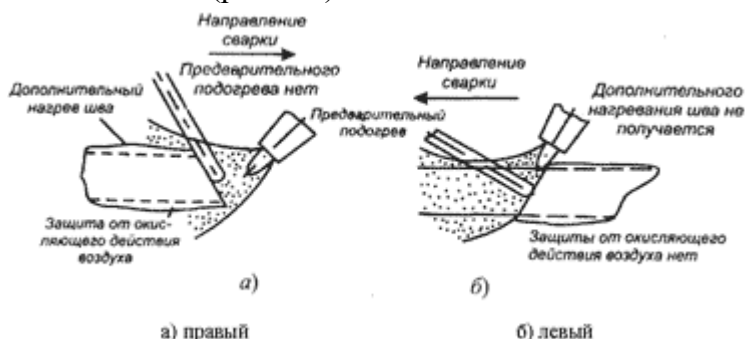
Способы перемещения горелки (способы газовой сварки)
